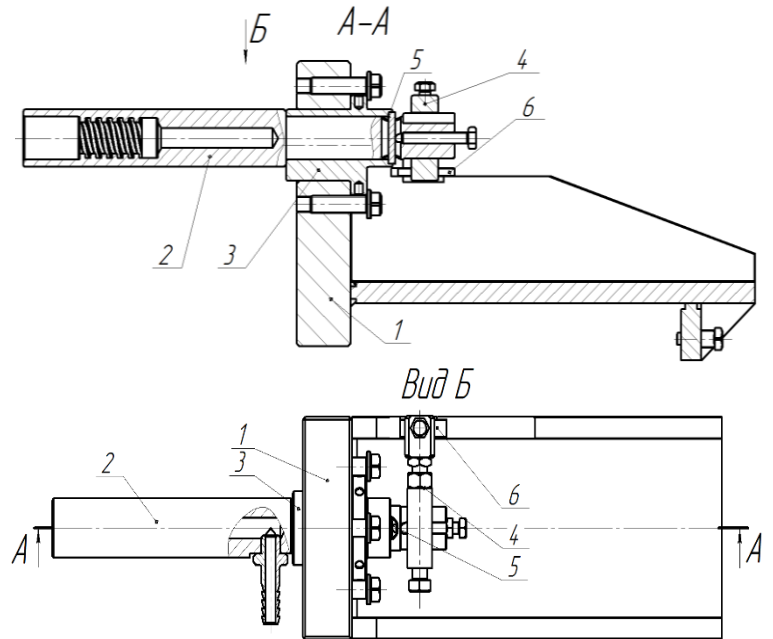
Конструктивна схема спеціального динамометричного пристрою: 1 – корпус; 2 – оправка; 3 – ексцентрикова втулка; 4 – важіль; 5, 6 – тензометричні балки
